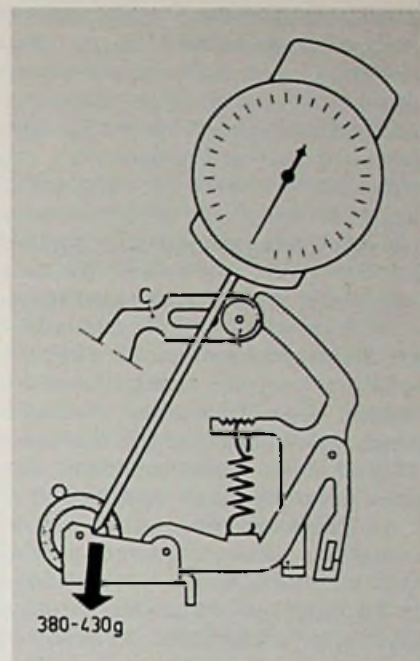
So wird mit einer Federwaage der Andruck der Gummirolle gemessen (Philips)
